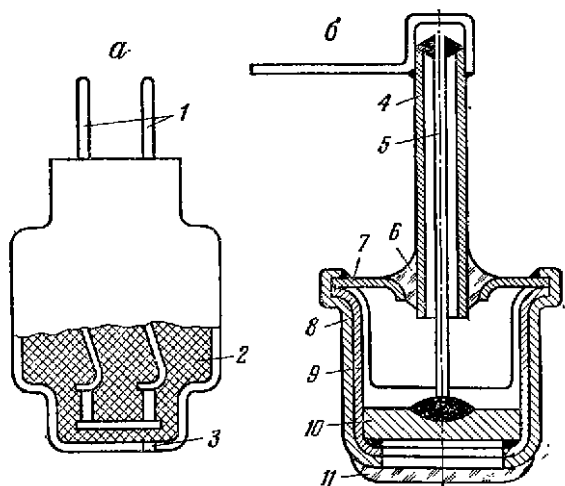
Фотокатоды в пластмассовом (а) и в металлическом (б) корпусе: 1 — выводы; 2 — пластмасса; 3 — отверстие для прохода излучения; 4 — металлическая труба; 5 — вывод; 6 — изолятор; 7 — крышка; 8 — металлический корпус; 9 — кристаллодержатель; 10 — монокристалл германия; 11 — выходное окно, закрытое стеклом.
